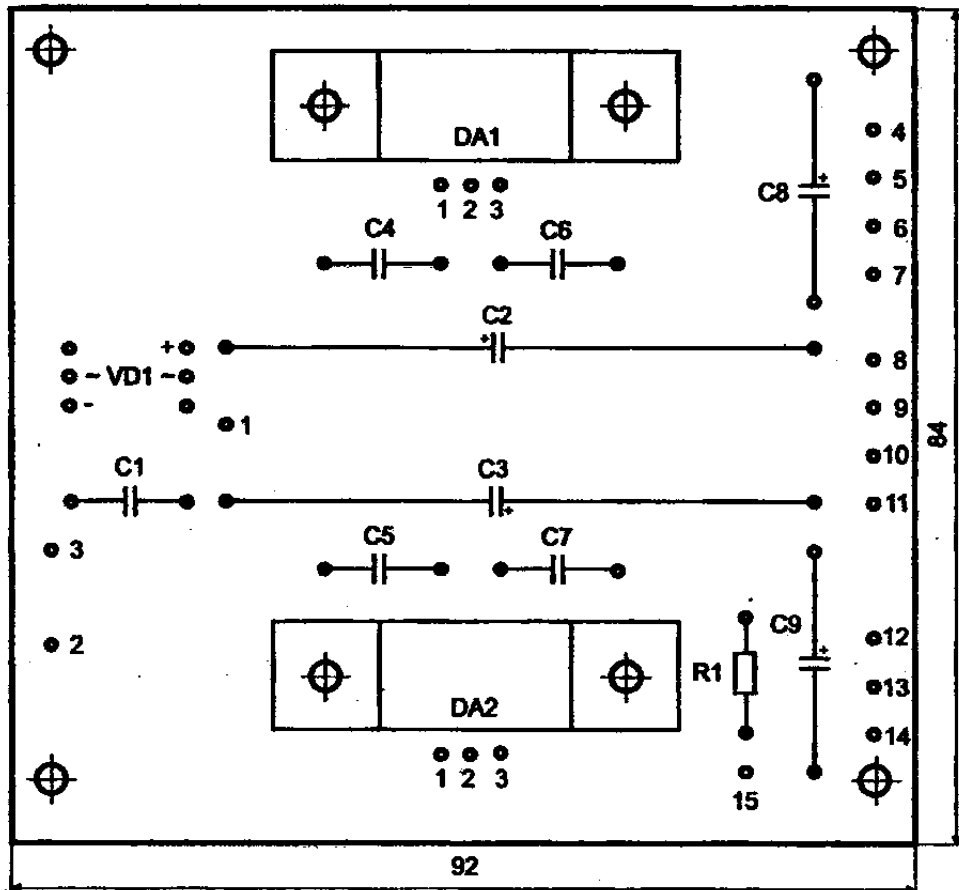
, б. Розташування деталей на платі стабілізатора
